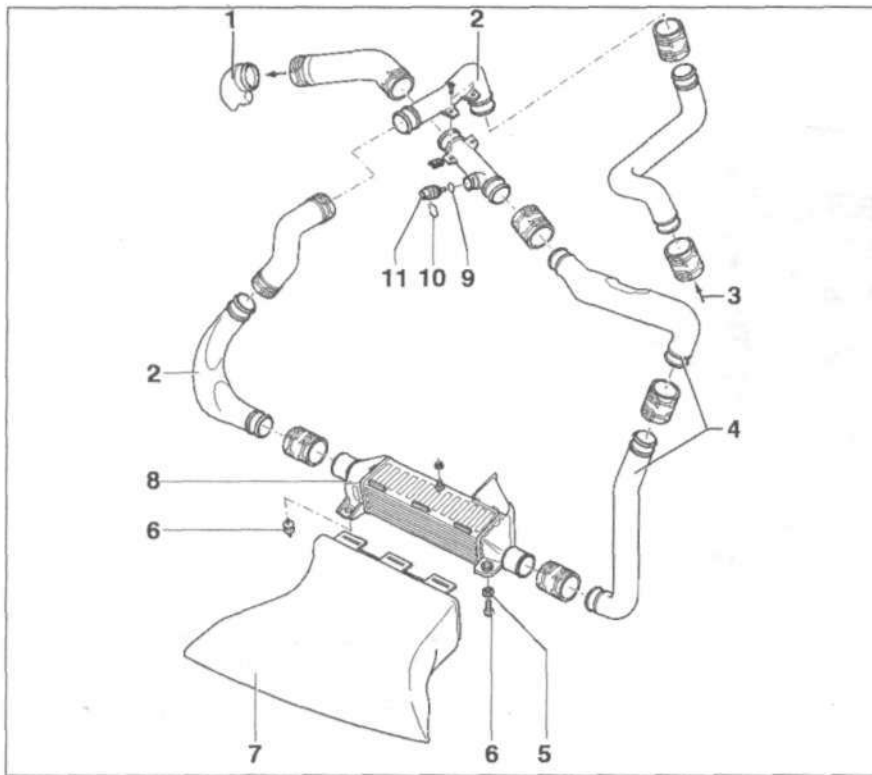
а. Турбокомпрессор с присоединяемыми элементами двигателей АНУ, АLE:
